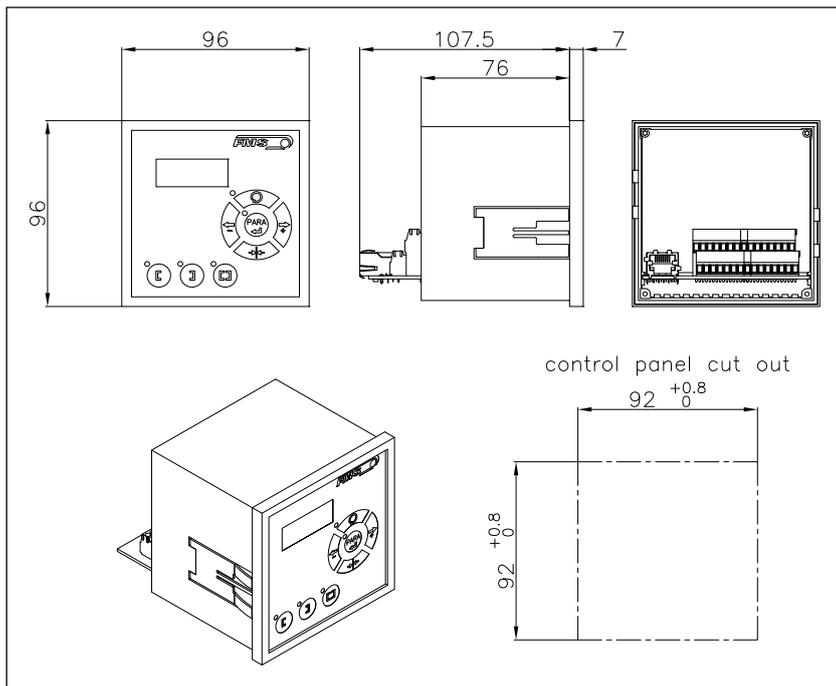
Mechanische Abmessungen BKS309.S Einbauversion
